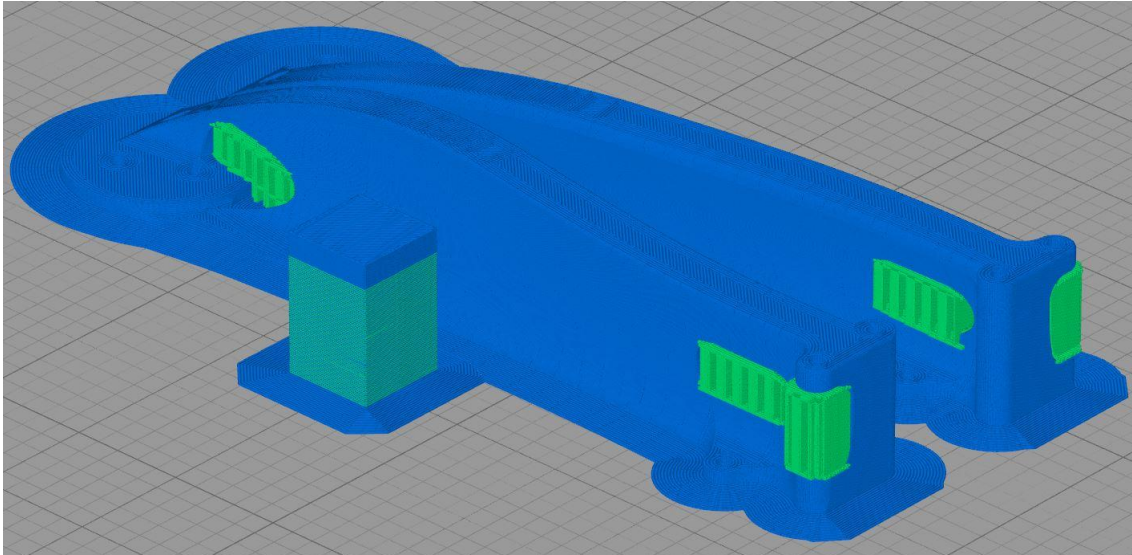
Herramientas utilizadas durante la impresión. Tool 1 será la pieza estructural, tool 2 fabricará el material de soporte. En la torre de limpieza se realizan capas alternativas de ambas herramientas y materiales.
